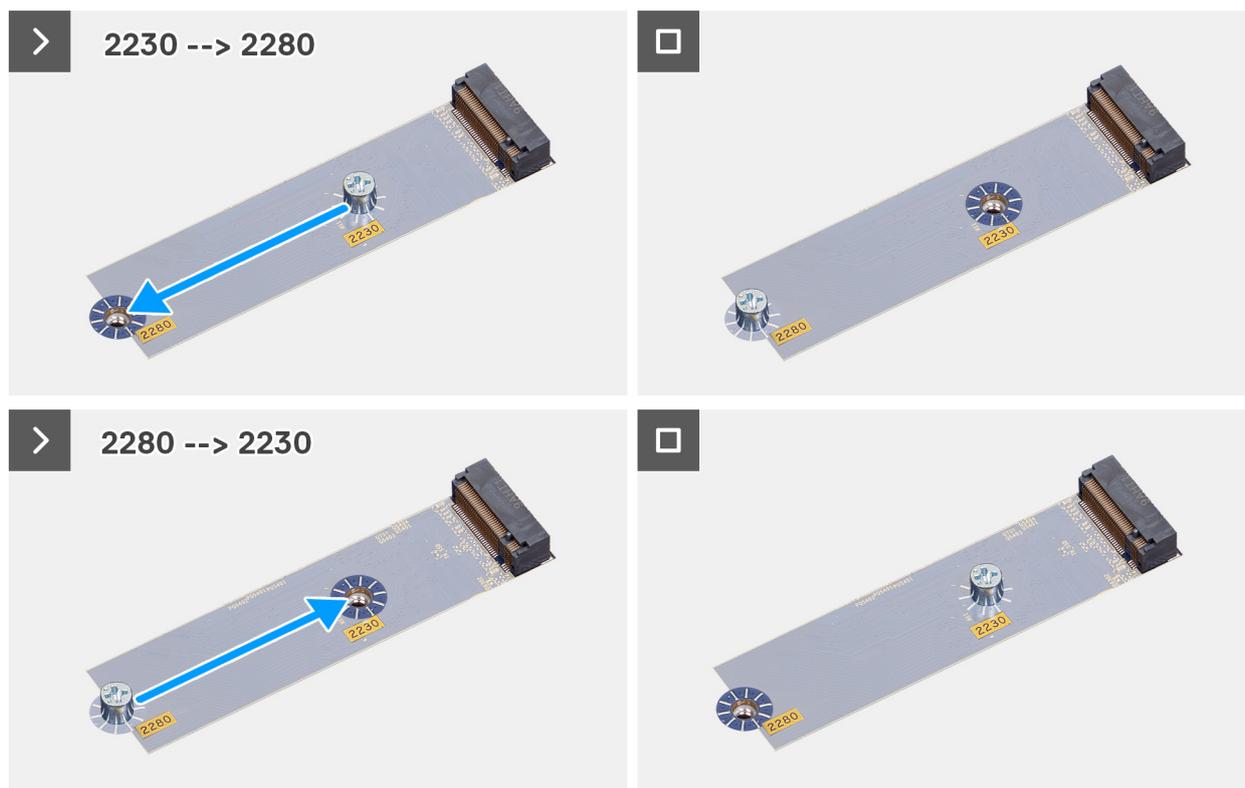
Spostamento della vite di montaggio nel montaggio della vite per unità SSD M.2 2280
